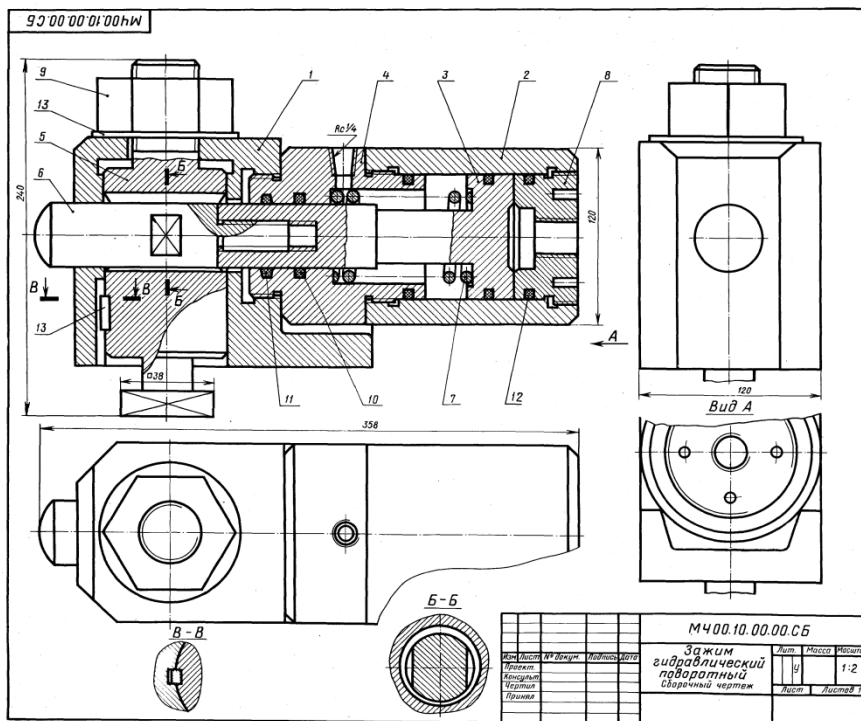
Сборочный чертеж «Зажим гидравлический поворотный»
